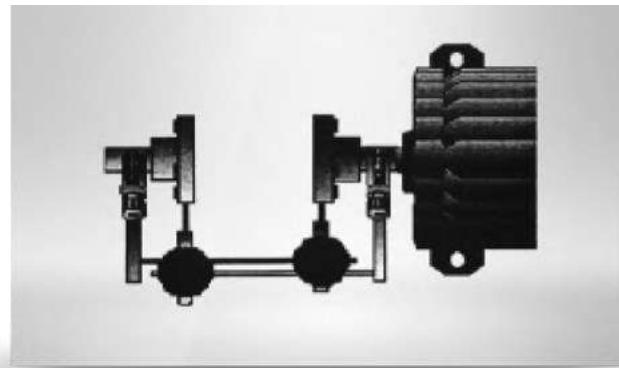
Вид сверху. Индикаторы в положении 9:00
